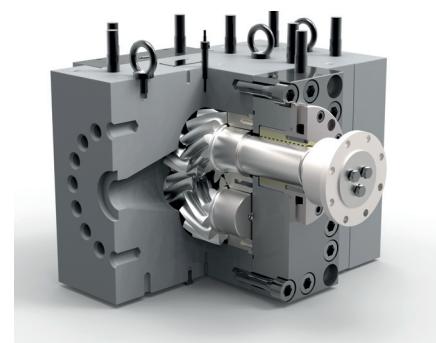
Насос EXTRU 716-110-110 с шевронным зацеплением в разрезе
